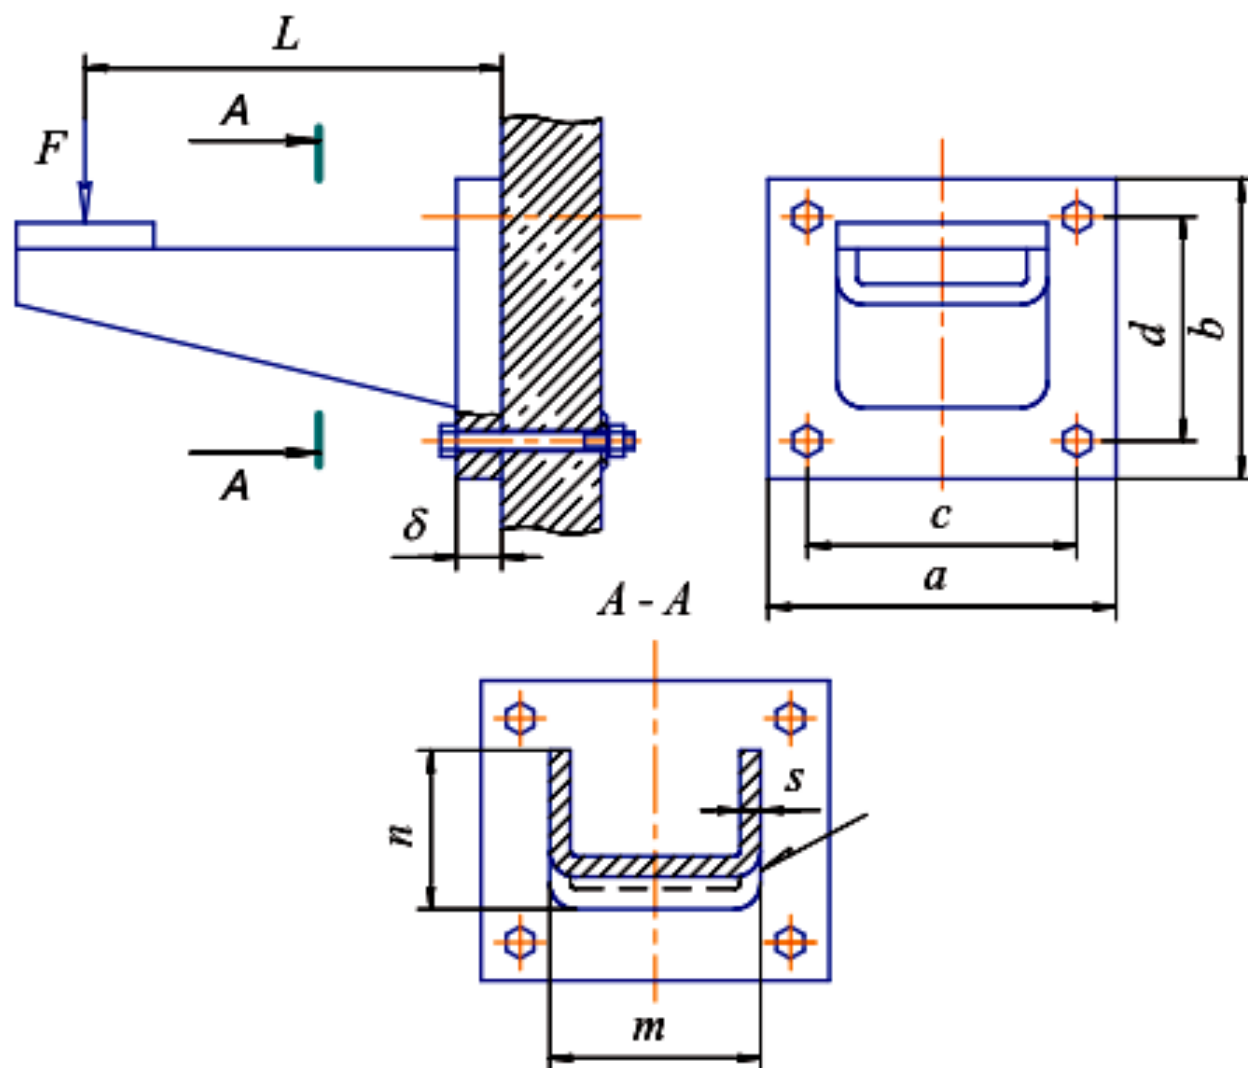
Сварной кронштейн, прикрепленный к бетонной стене
